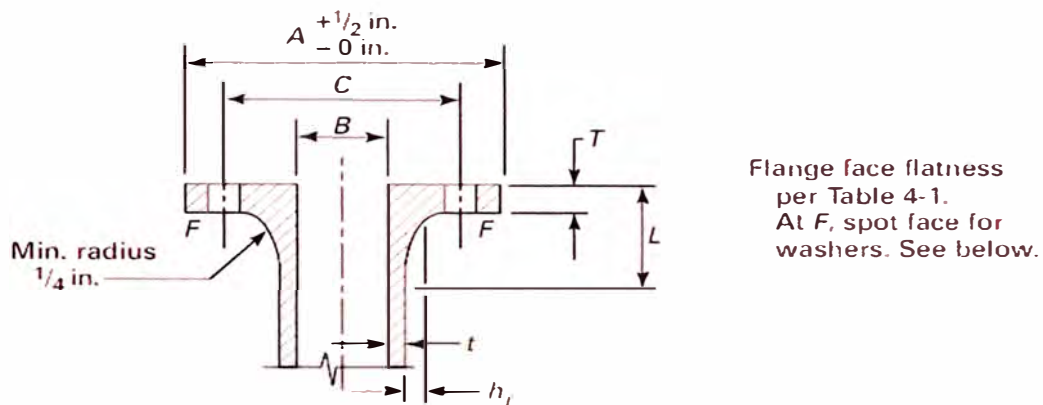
BRIDAS DE CARA PLANA CONSTRUIDAS CON FRP
